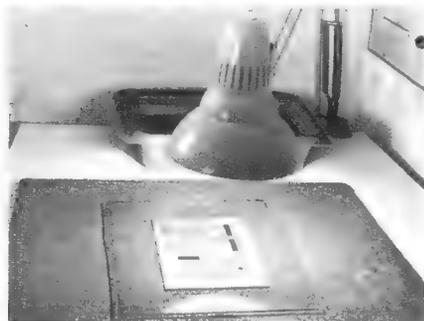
Zum Belichten werden Vorlage und fotobeschichtete Platte mit einer Glasplatte beschwert, um guten Kontakt zu gewährleisten, damit die Kanten der Zeichnung sauber herauskommen
